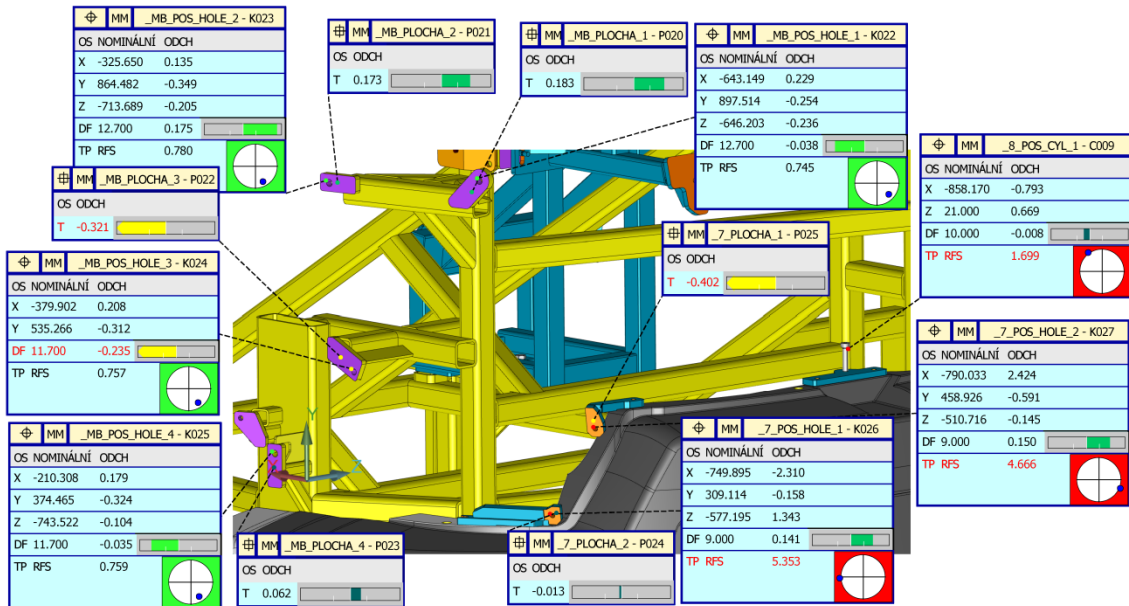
Rozměrová kontrola přípravku 2/6
